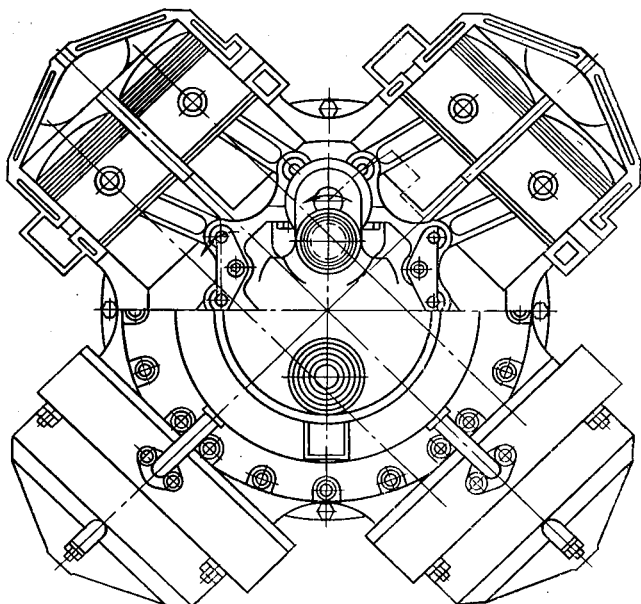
Конструктивная схема двигателя Дина-Стар с параллельным расположением цилиндров
